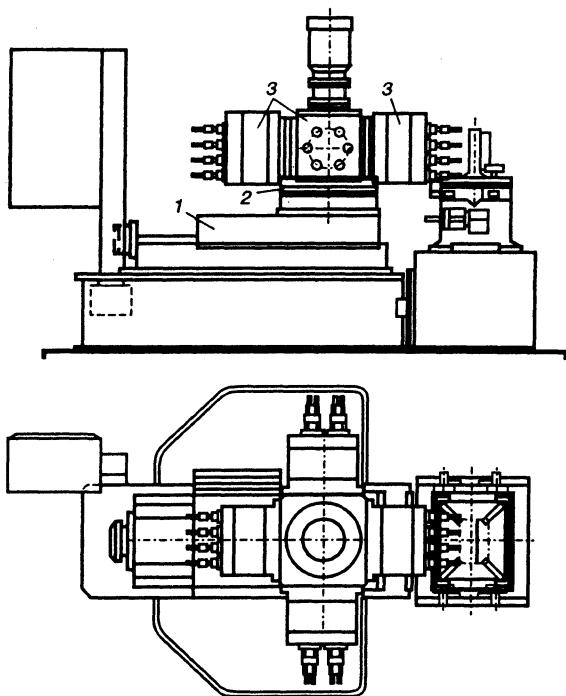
Переналаживаемый агрегатный станок с многошпиндельными коробками:
